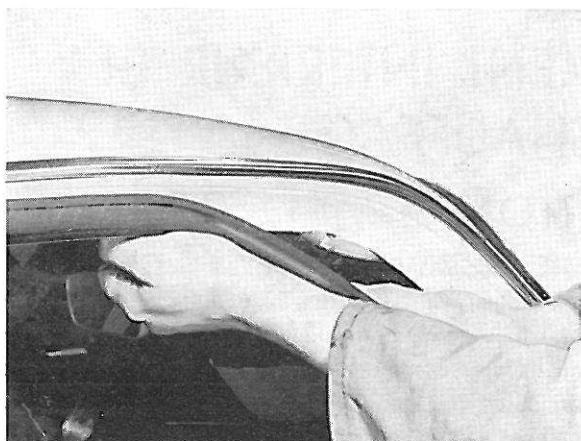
Mise en place d'un joint d'étanchéité d'encadrement de porte
